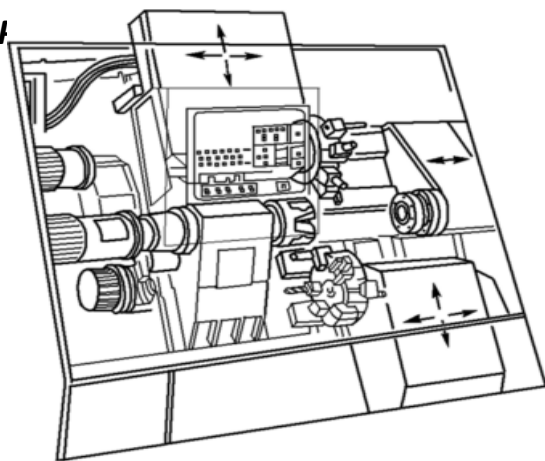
Инструментальная система с револьверными головками токарного ГПМ
